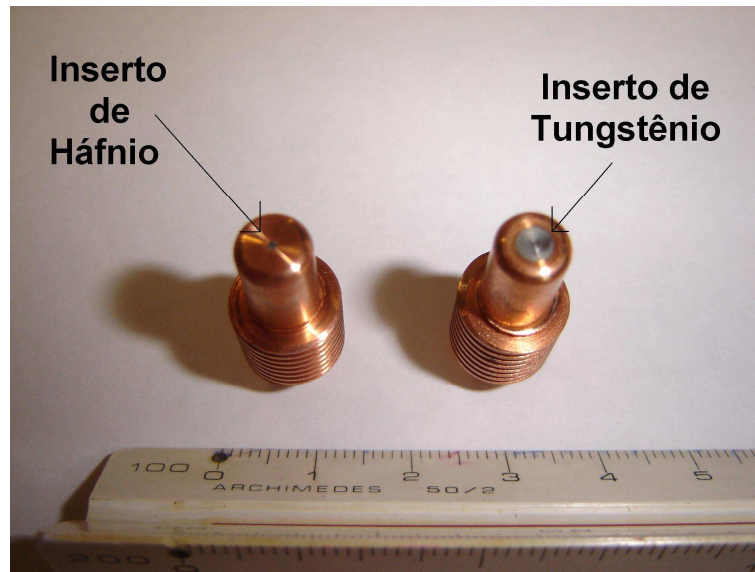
Eletrodo de cobre com inserto de háfnio (esquerda) e o inserto de tungstênio (direita).
